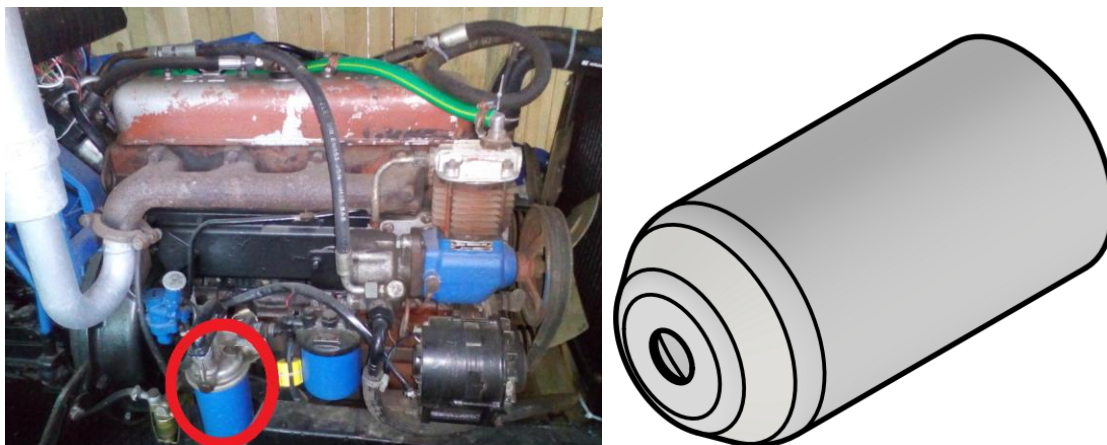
Príklady výrobkov zhotovených hlbokým ťahaním [5; 6; 7].
